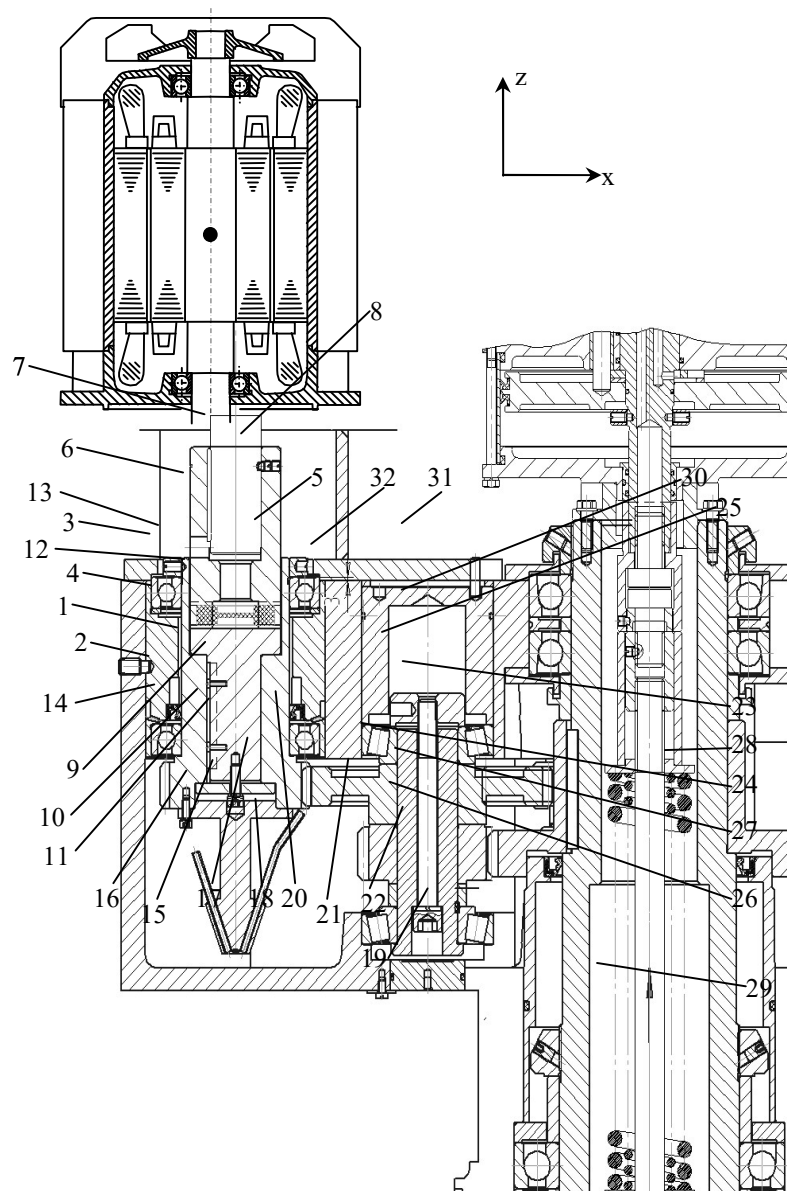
Бабка шпиндельна базового вертата ПАБ350
